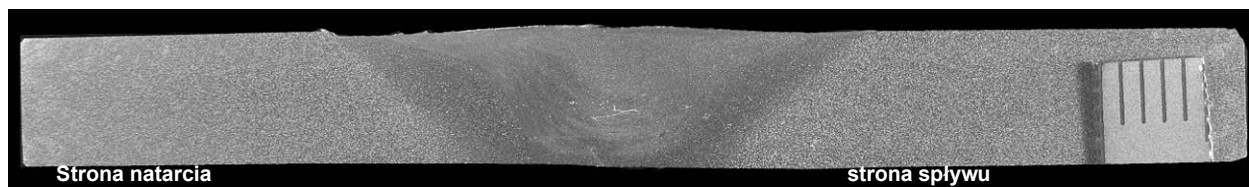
Makrostruktura złącza FSW ze stopu aluminium EN AW-6082. Parametry zgrzewania: $V_n = 1800$ obr/min, $V_z = 1120$ mm/min
